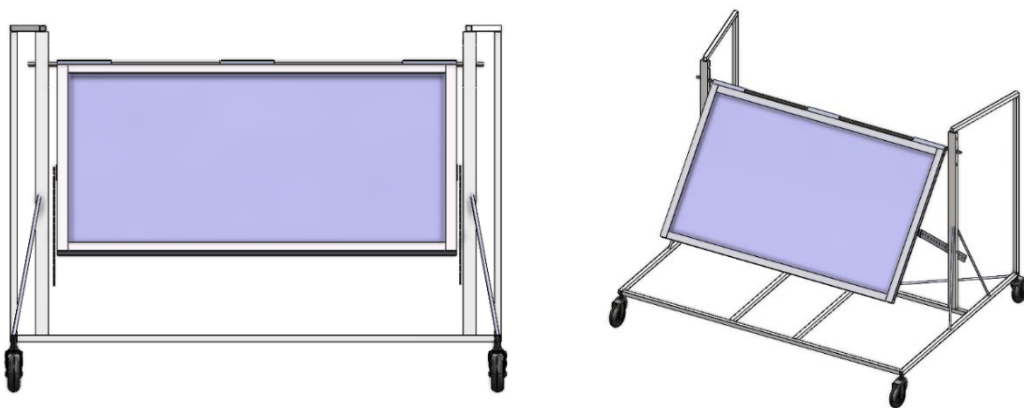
Vista frontale (sx) e isometrica (dx) del carrello
